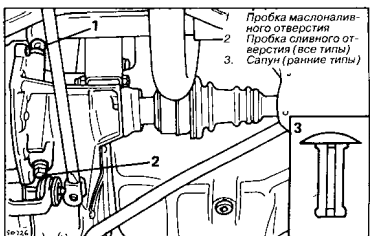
Расположение пробки маслониливного отверстия коробки передач (ранний тип) и пробки сливного отверстия (все типы)
